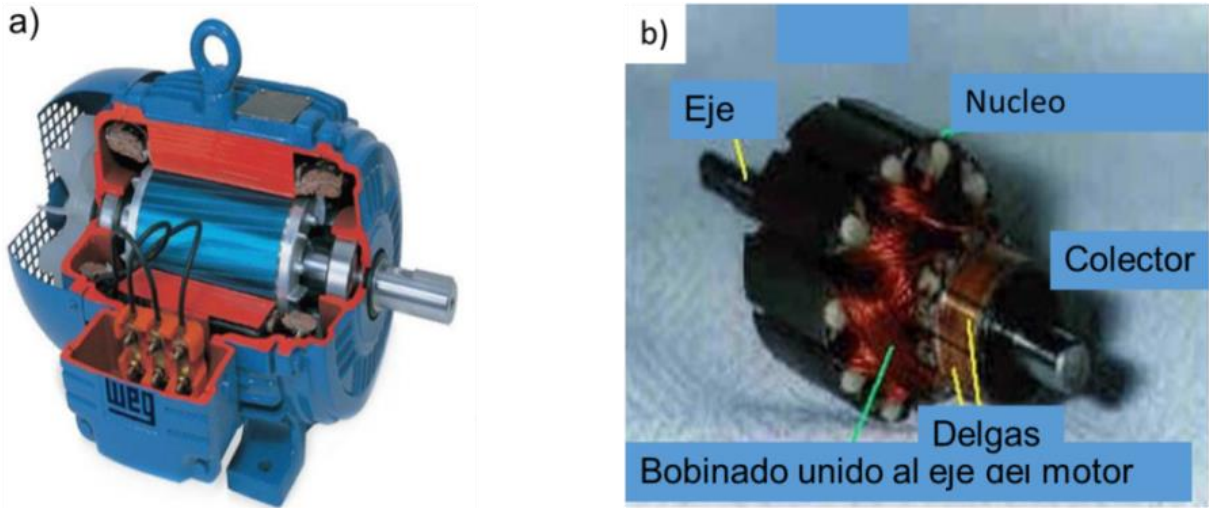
Tipos de rotor, a) integrado a motor eléctrico trifásico marca weg, y b) componentes principales [11]
